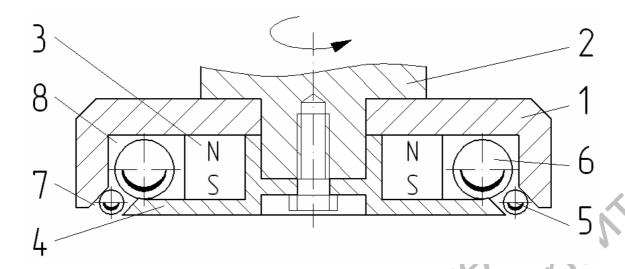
Двухрядный инструмент для магнитно-динамического упрочнения плоских поверхностей
